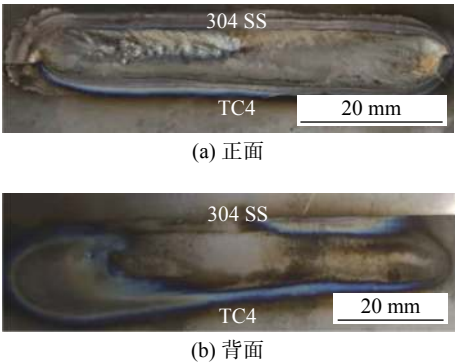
TC4/304 SS 搭接焊接头的焊缝形貌
